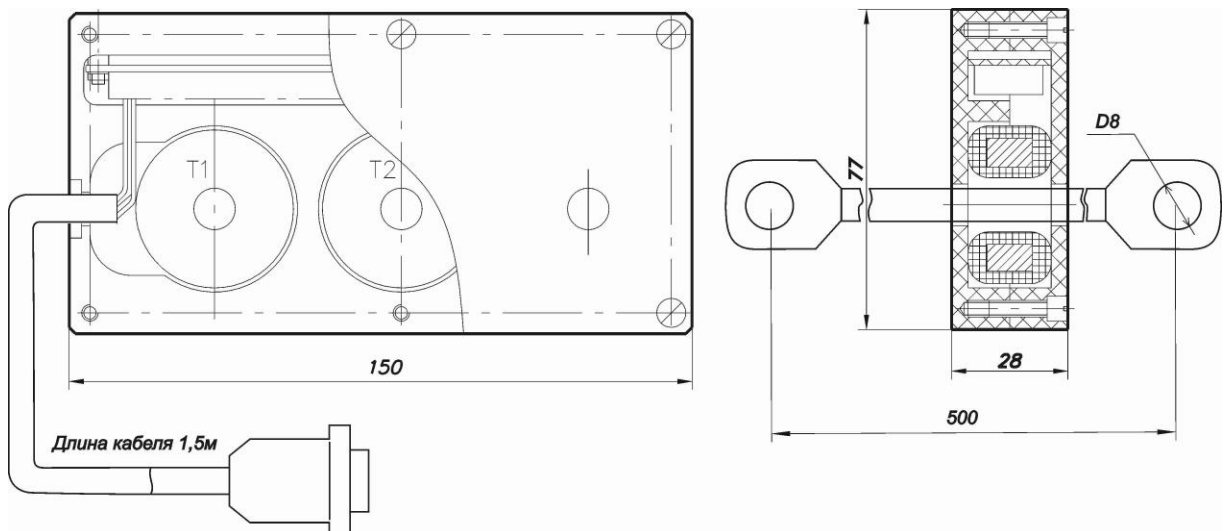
Габаритно-присоединительные размеры датчика тока и напряжения
